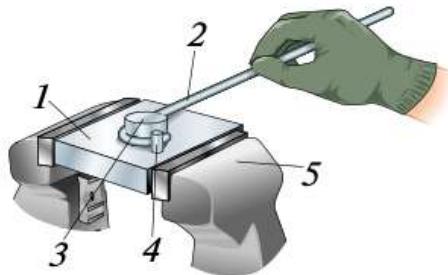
Гибка проволоки в приспособлении в слесарных тисках: 1 — приспособление; 2 — заготовка; 3 — оправка; 4 — упор; 5 — слесарные тиски
